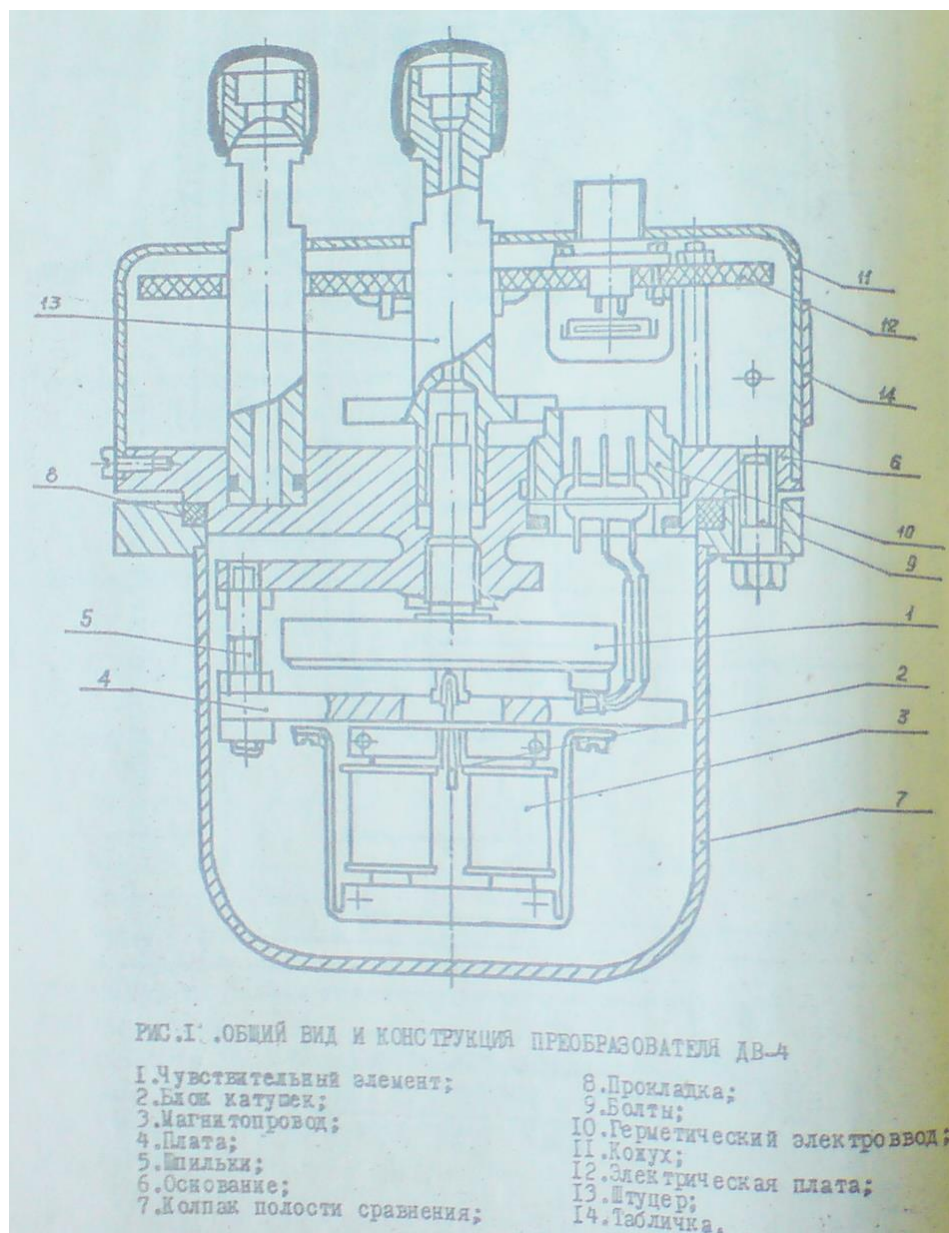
Общий вид и конструкция преобразователя ДВ-4.
